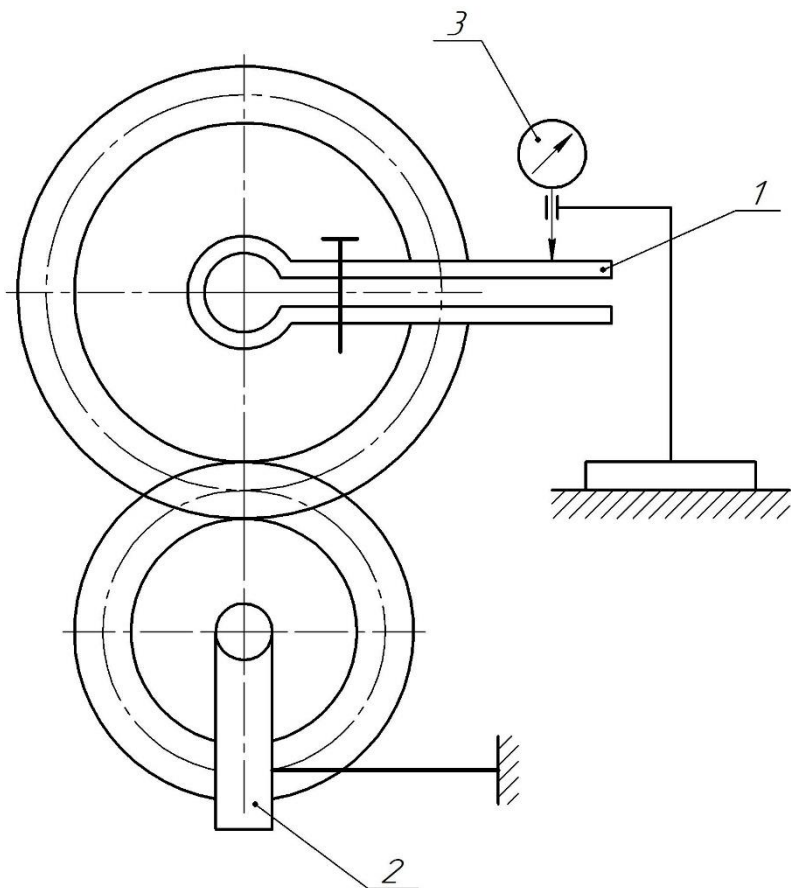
Схема контролю бокового зазору в зубчастому з'єднанні: 1 – оправка; 2 – пристрій; 3 – індикатор
